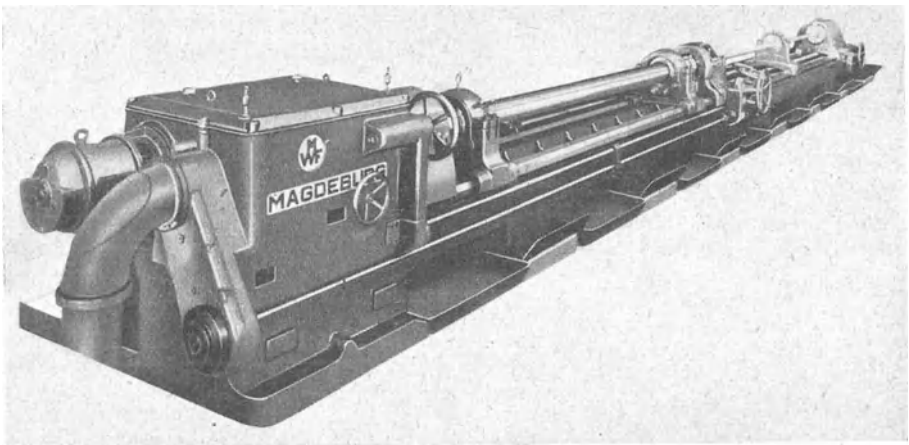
Tieflochbohrmaschine für große Bohrungen bis 220 mm \varnothing . (Magdeburger Werkzeugmaschinenfabrik.)
